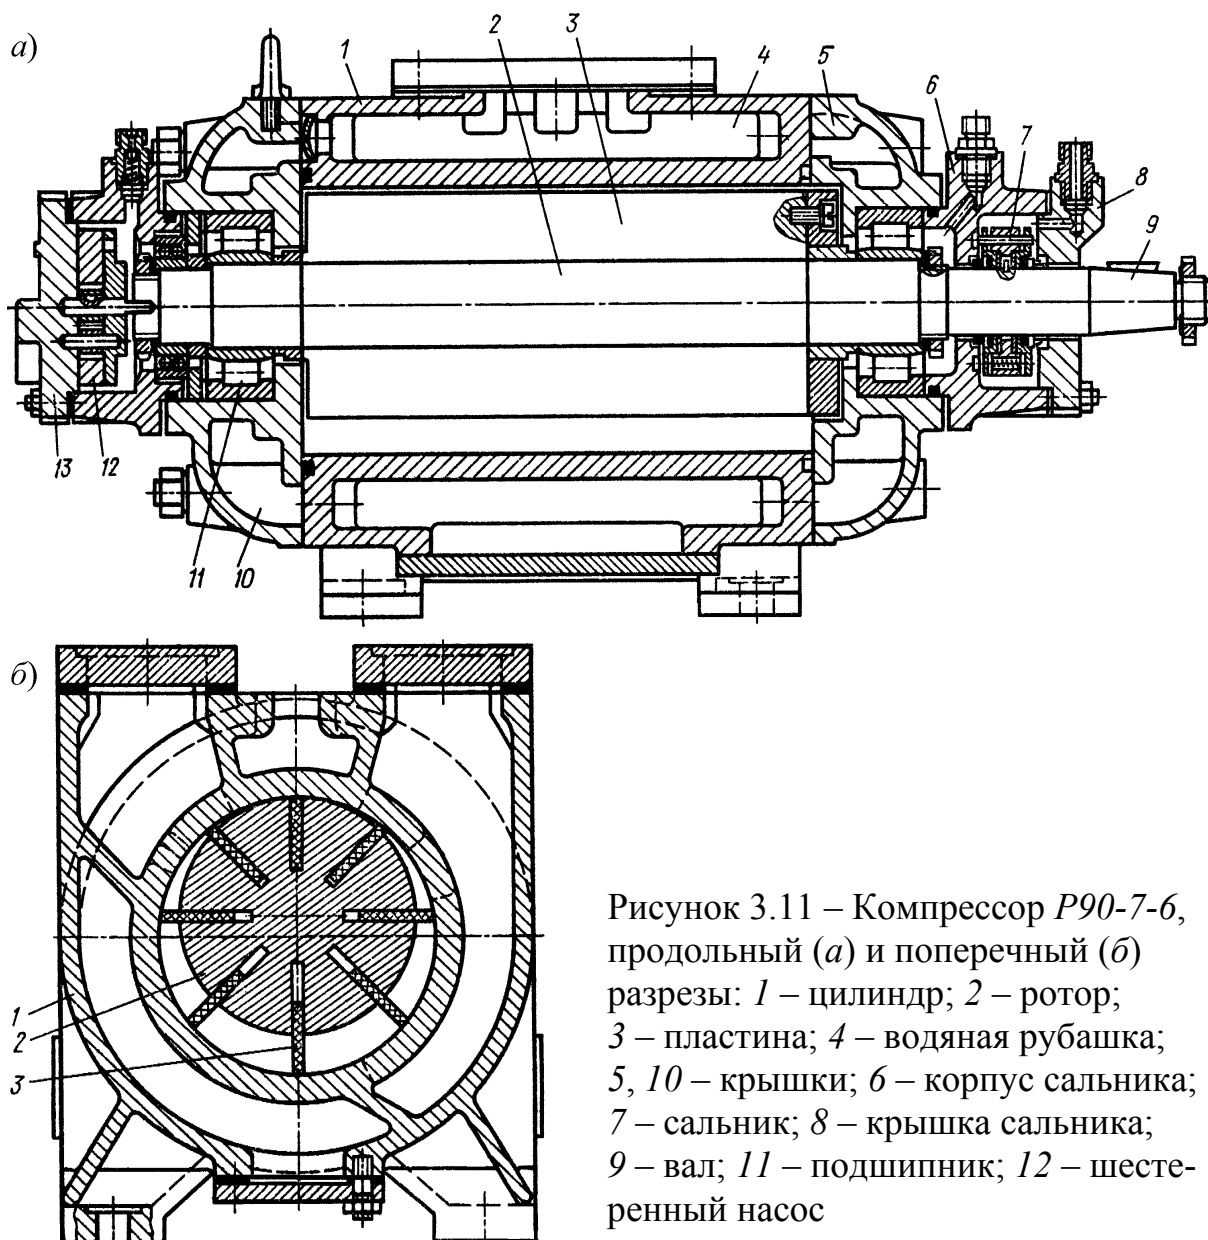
Компрессор P90-7-6, продольный (а) и поперечный (б) разрезы: 1 – цилиндр; 2 – ротор; 3 – пластина; 4 – водяная рубашка; 5, 10 – крышки; 6 – корпус сальника; 7 – сальник; 8 – крышка сальника; 9 – вал; 11 – подшипник; 12 – шестеренный насос
